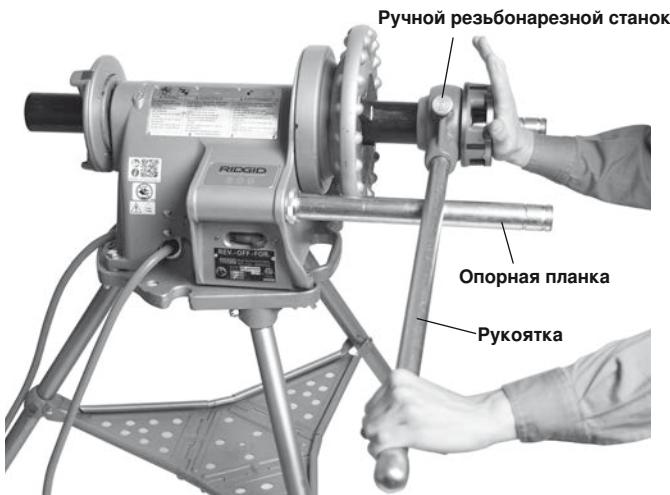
Нажатие ручного резьбонарезного станка на трубу для зацепления гребенок
